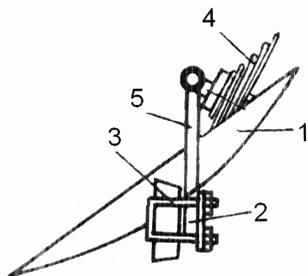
Общий вид дискового почвообрабатывающего орудия (вид сверху)
